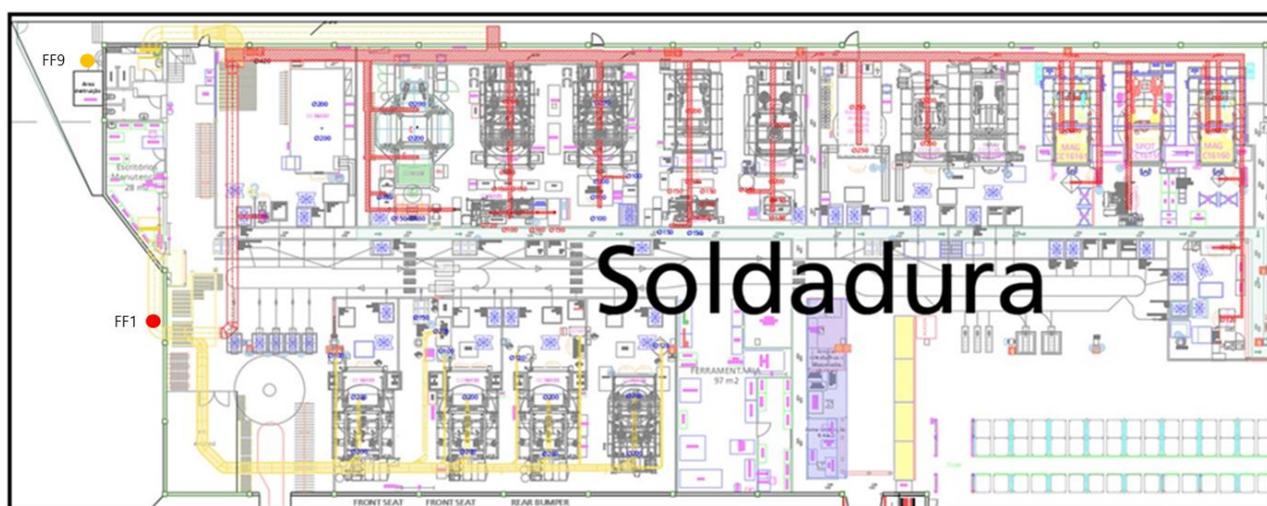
Detalhe do layout da soldadura em vigor após 2017
